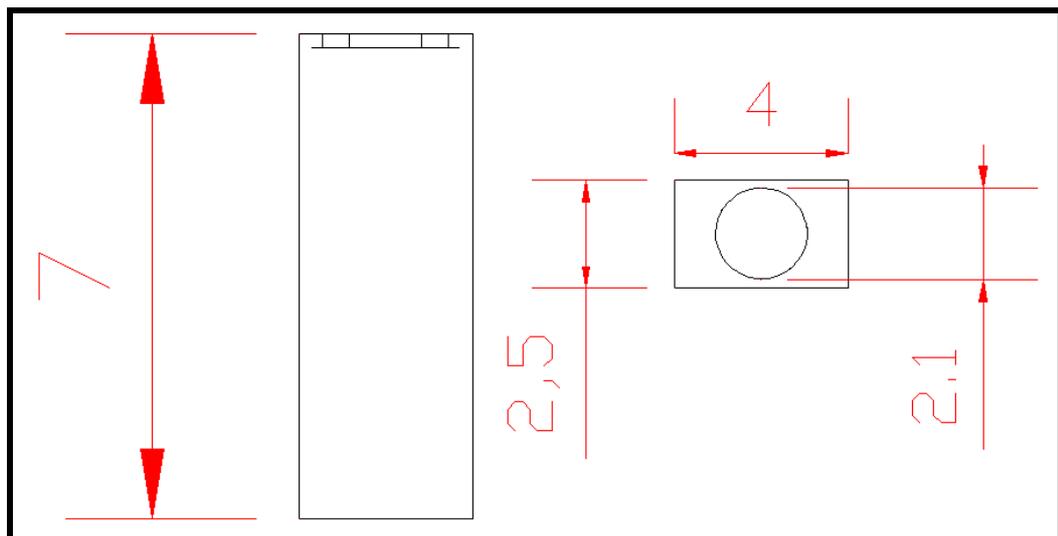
Vista Superior y Lateral del Rectángulo (Dimensiones en cm.)
